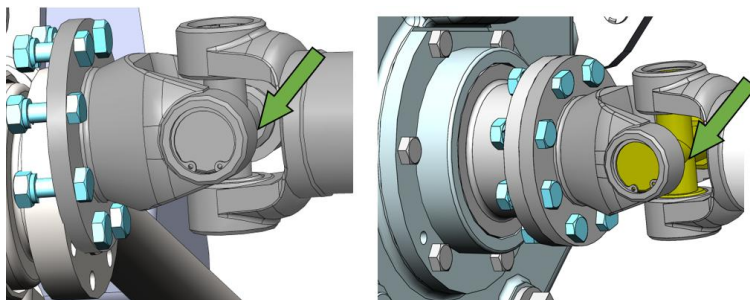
Расположение пресс-масленок на крестовине карданного вала
